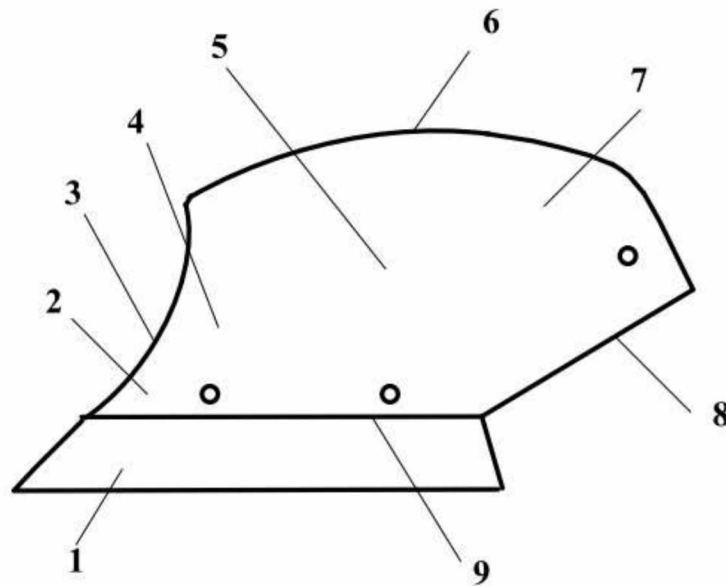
Корпус плуга: 1 – леміш; 2 – носок; 3 – польовий обріз; 4 – груди; 5 – робоча область; 6 – верхній обріз; 7 – крило; 8 – борозний обріз; 9 – стикового обріз
